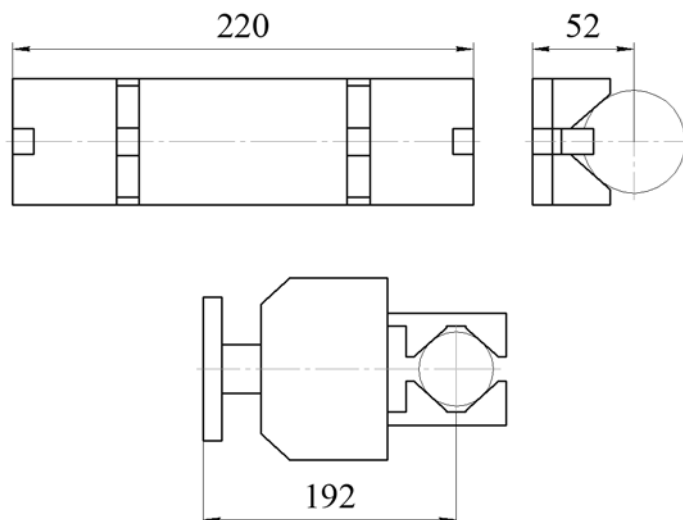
Положения заготовки при создании рабочей системы координат
